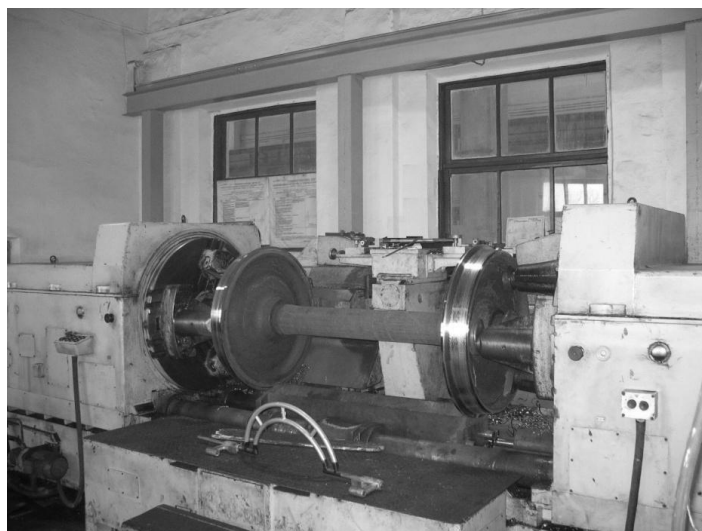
Общий вид колесотокарного станка КЖ1836
